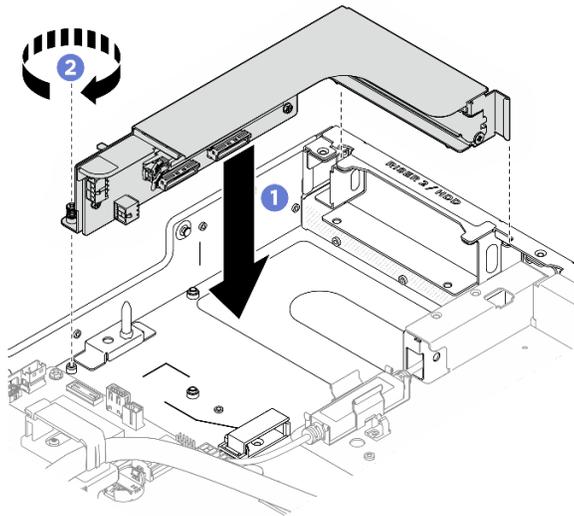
Installation de l'assemblage de cartes mezzanines PCIe dans l'emplacement 2
